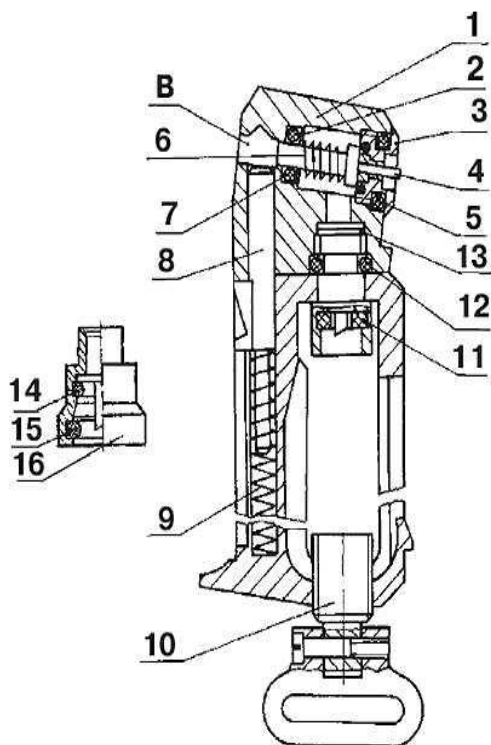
Схема магазина пистолета МР-654К: 1 — корпус клапана; 2 — шайба; 3 — седло клапана; 4 — клапан; 5 — кольцо; 6 — пружина клапана; 7 — кольцо клапана; 8 — подаватель; 9 — пружина подавателя; 10 — винт поджимной; 11 — элемент уплотнительный; 12 — кольцо уплотнительное; 13 — фильтр; 14 — кольцо; 15 — кольцо уплотнительное; 16 — переходник; В — загрузочное отверстие
